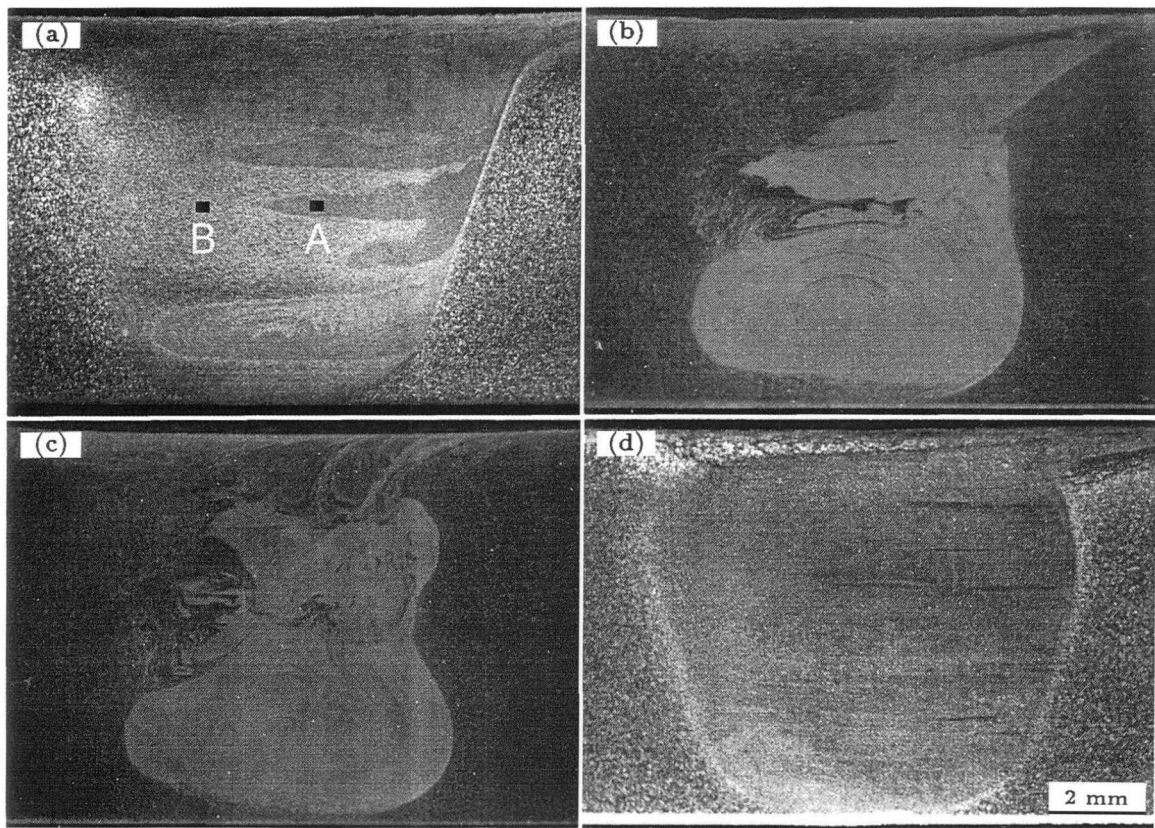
22 mm 直径轴肩配合 8 mm 直径圆锥形搅拌针加工的 7075 铝合金截面的宏观形貌
